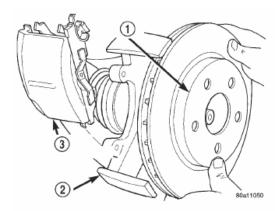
Instalación del calibrador del freno de disco y del rotor
